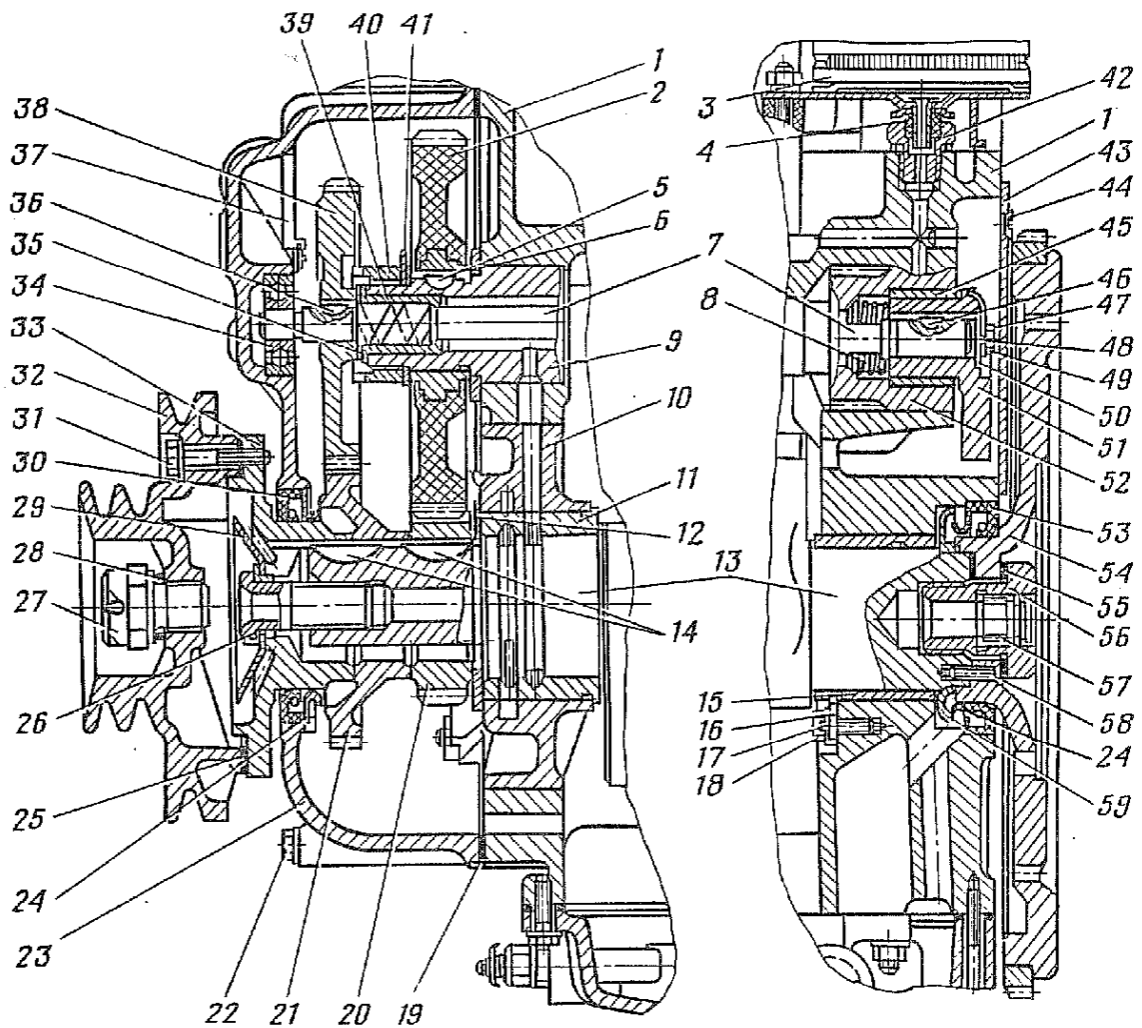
Привод распределительного вала и балансирного механизма, задний коренной подшипник:
